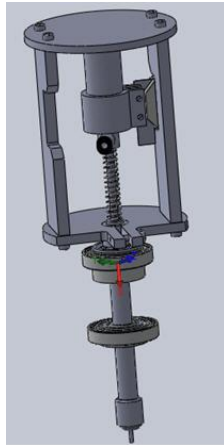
โครงสร้างส่วนยึด Ball Bearing และ Roller Bearing
